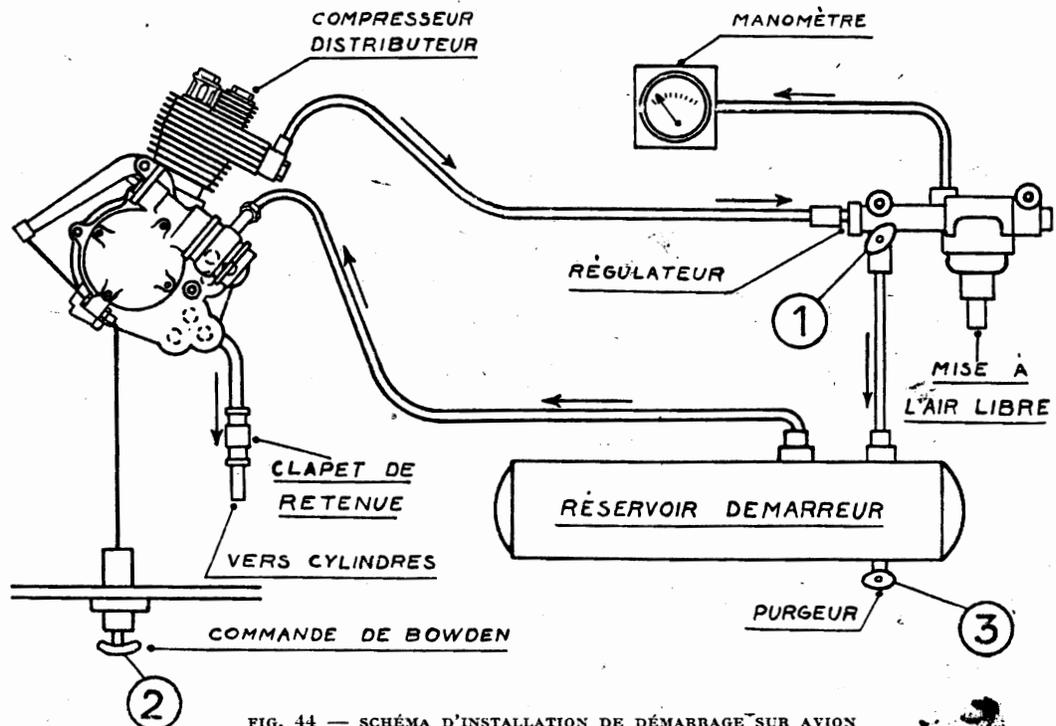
SCHÉMA D'INSTALLATION DE DÉMARRAGE SUR AVION
